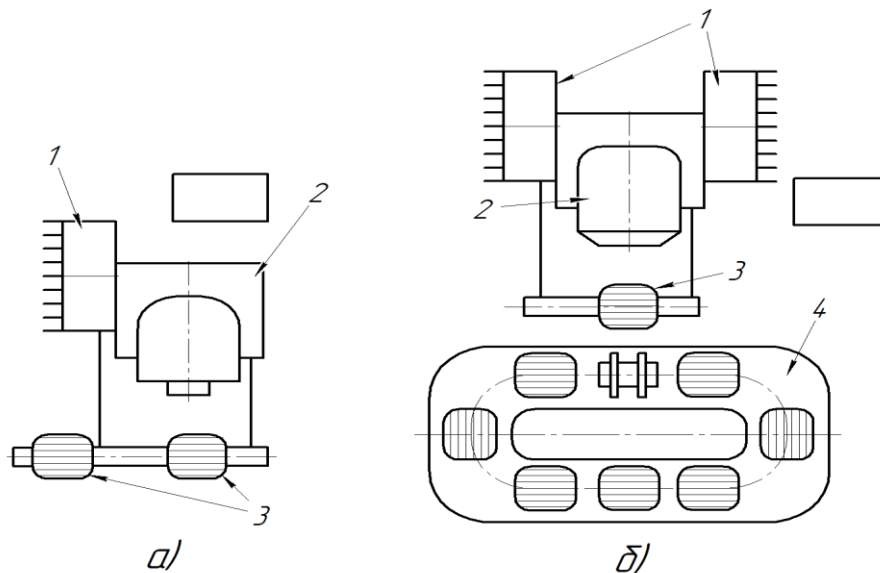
Гнучкий виробничий модуль, що містить один верстат з ЧПК: *а* – з двома маятниковими робочими столами; *б* – з автоматизованим завантажувальним пристроєм; 1 – магазини з інструментами; 2 – верстат з ЧПК; 3 – стіл верстата; 4 – автоматизований завантажувальний пристрій (кроковий конвеєр – накопичувач палет)
